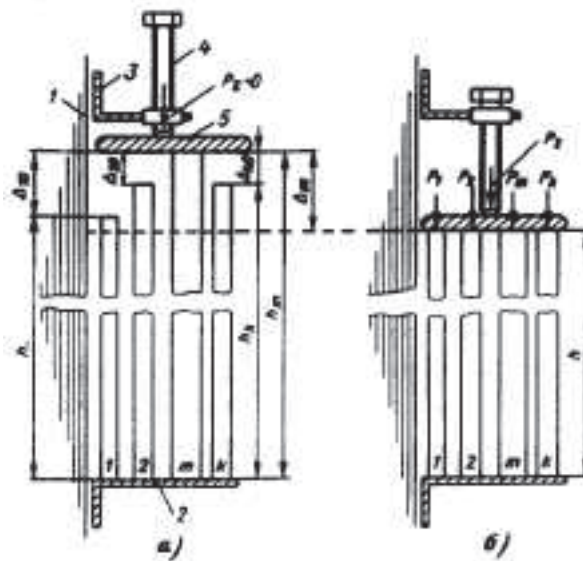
Схематическое расположение обмоток до запрессовки (а) и после запрессовки (б) общим кольцом: 1 — магнитопровод; 2 — нижняя прессующая балка; 3 — верхняя прессующая балка; 4 — прессующий болт; 5 — прессующее кольцо
